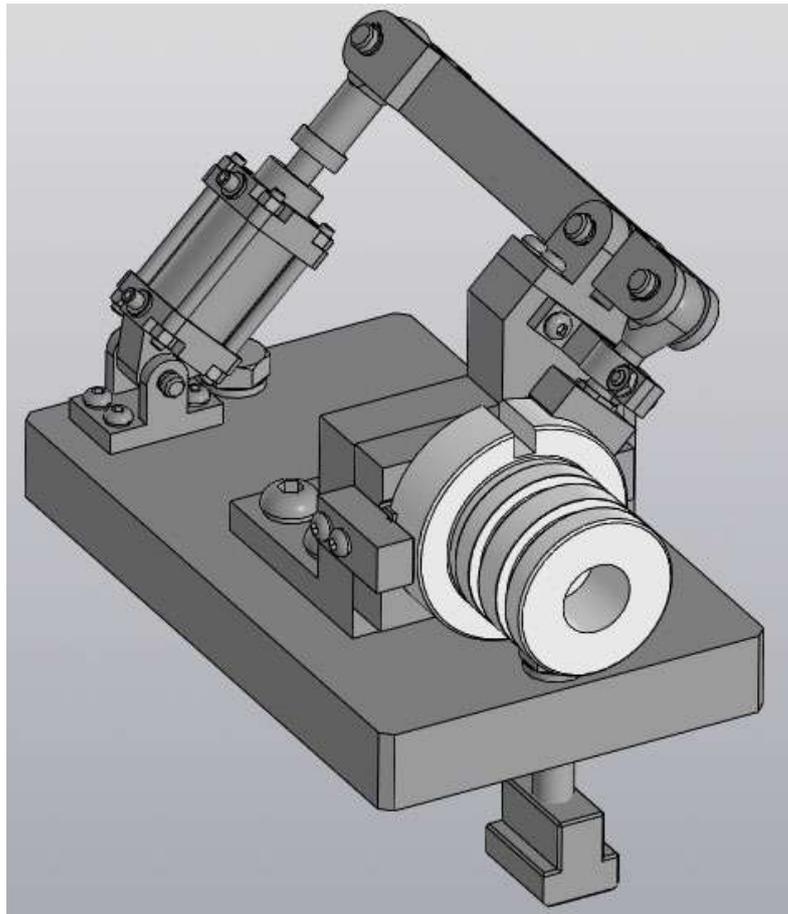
Конструкция приспособления с заготовкой, вид 1
